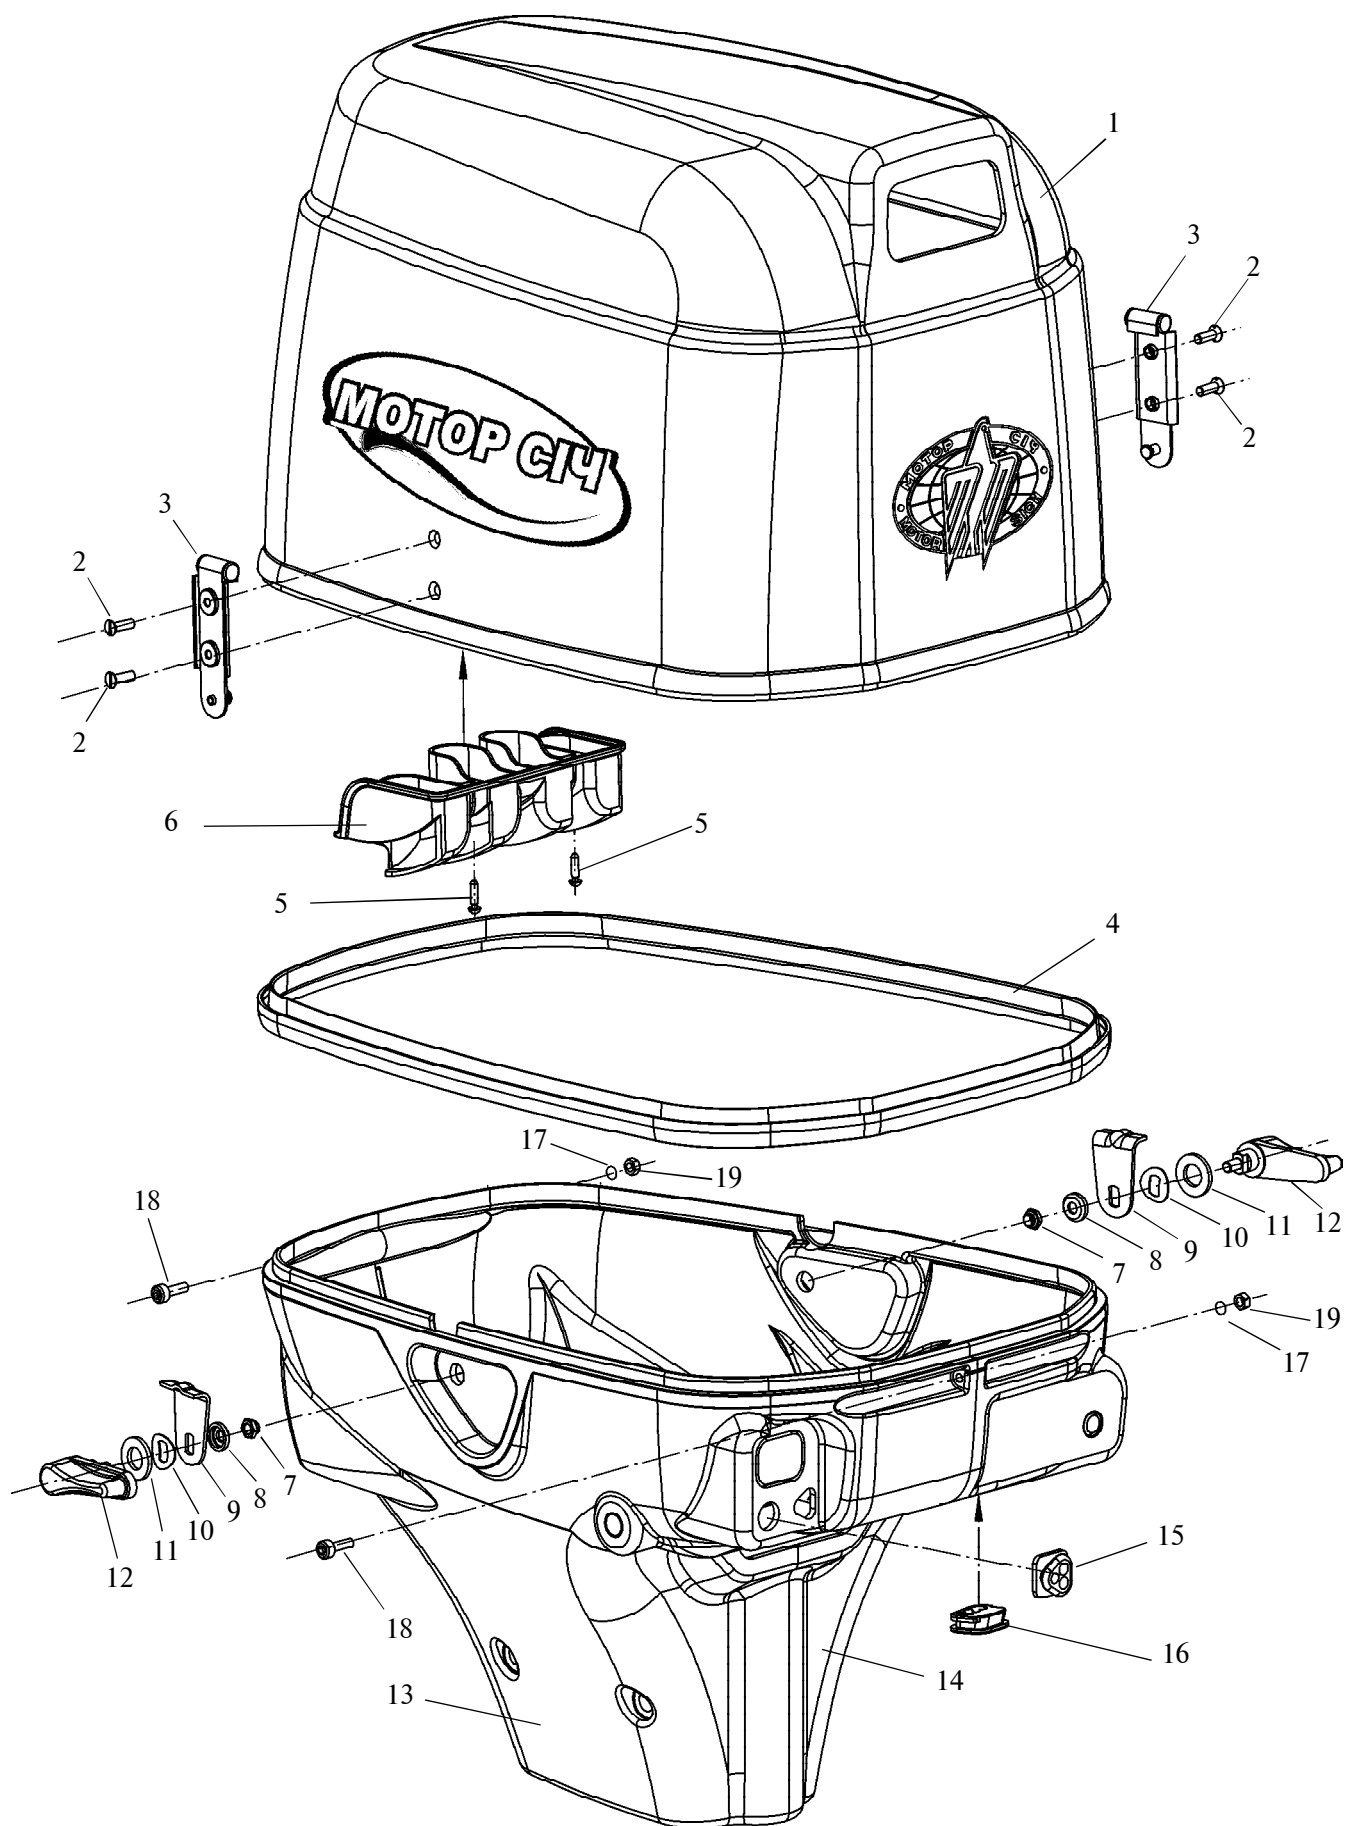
Колпак, корпус замка мотора лодочного подвесного «Мотор Січ ПЛМ-40Э»
